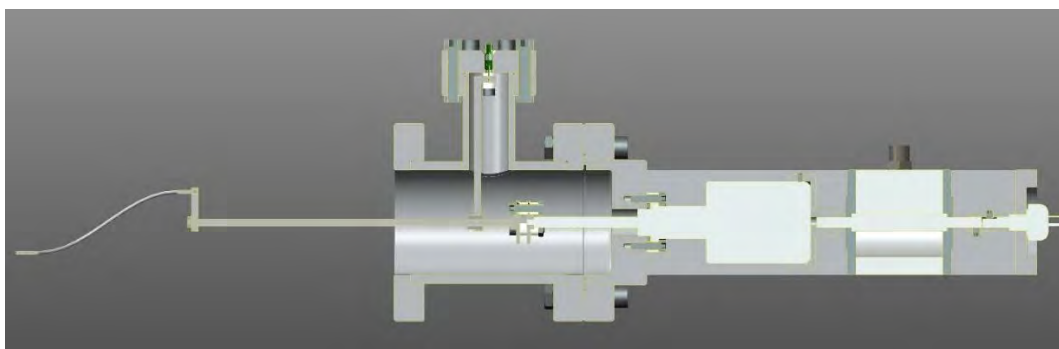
vista in sezione del Beam-Profiler nella soluzione finale
